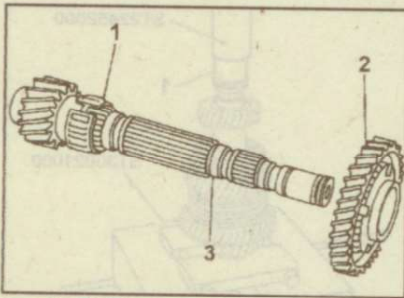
Установка игольчатого подшипника (1) и шестерни 1-й передачи (2) на вторичный вал (3)
